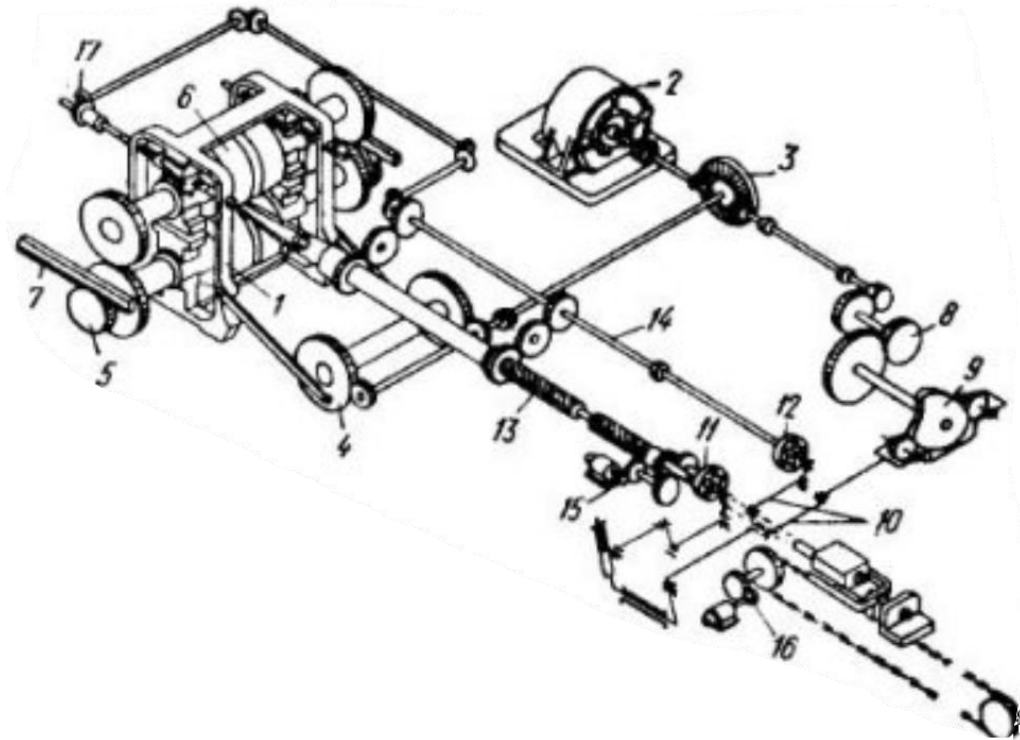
Кінематична схема стану типу ХПТ: 1-робоча кліть; 2- головний двигун; 3 – редуктор; 4 - кривошипно-шатунний механізм; 4 - валки; 5- ведуча шестерня; 6 - торці валків; 7- нерухомі шестеренчаті рейки;
